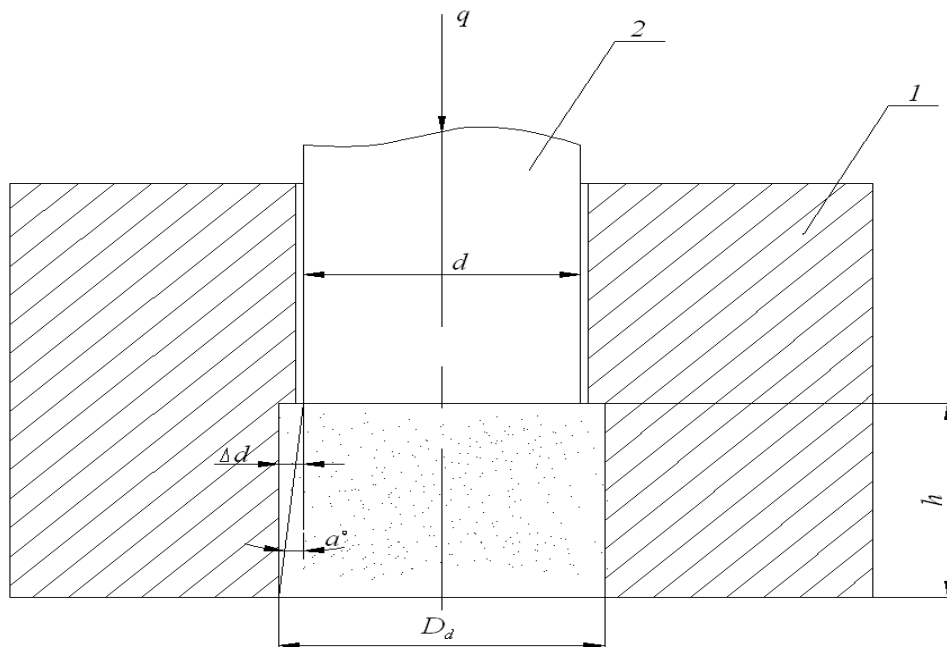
Пресс-форма цилиндрическая ступенчатая для прессования порошковых увлажненных смесей при изготовлении высокоплотных цилиндрических деталей высокой размерной точности: 1 – матрица; 2 – пуансон
